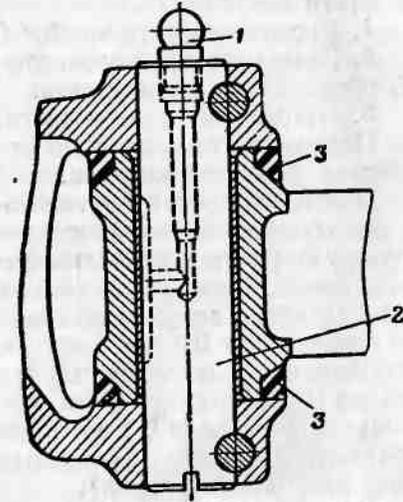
Соединение поперечной тяги управления с рычагами поворотных кулаков:
